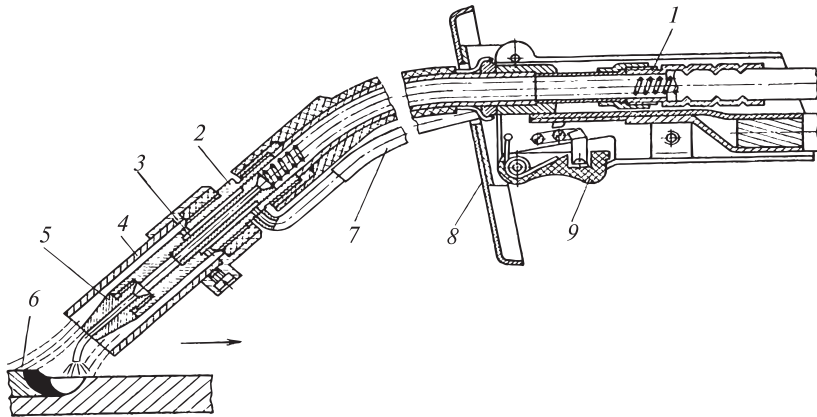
Устройство рабочей части горелки для сварки плавящимся электродом в среде защитных газов
